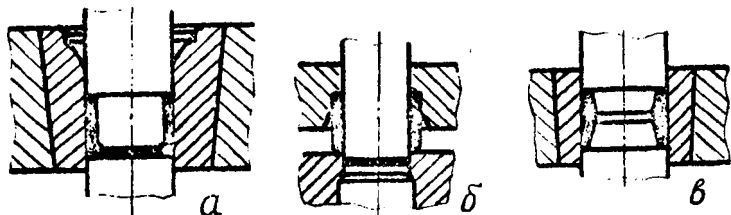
Схема технологического процесса изготовления втулок методом глубокой вытяжки стаканов с последующей пробивкой дна и формовкой конусных поверхностей: а - вытяжка стакана; б - пробивка дна; в - формовка конических поверхностей.
